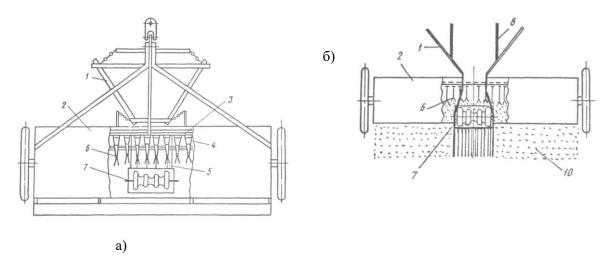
Конструкция описываемой сеялки по патенту № 523656 а) общий вид сеялки; б) процесс посева и образования валиков и почвенных борозд. 1-формирователь валиков; 2- сеялка; 3-рама; 4,5- поводки; 6- сошник; 7- профильный каток; 8-валик.
